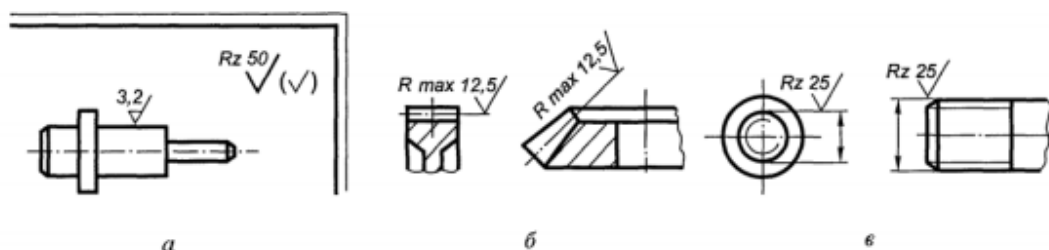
Простановка знака шероховатости: для всего изделия (а), на зубчатое колесо (б), резьбу (в)
